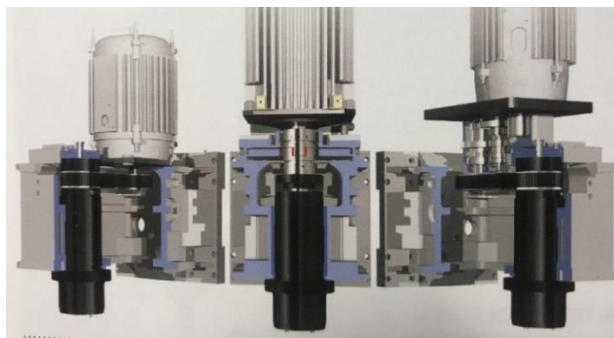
Шпинделі токарно-фрезерних обробних центрів
